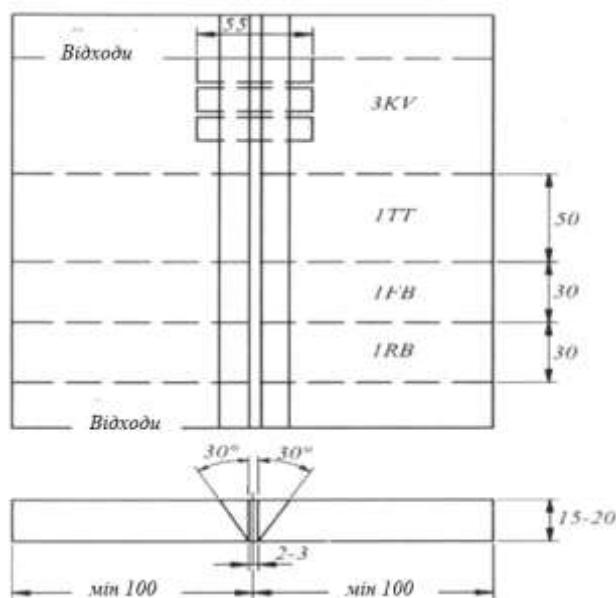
Проба стикового зварного з'єднання при випробуваннях електродів для ручного дугового зварювання.
